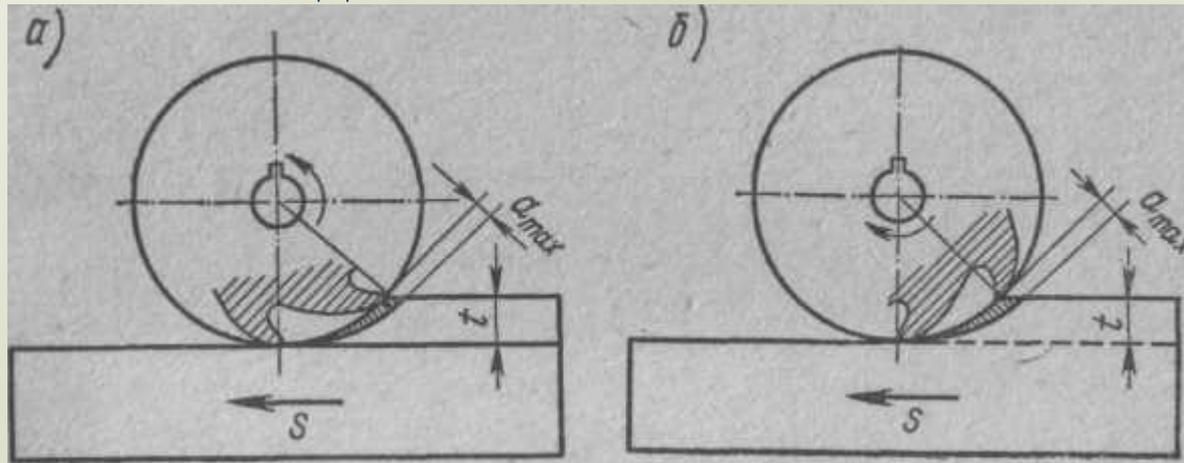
Схемы фрезерования: а — встречное; б — попутное
